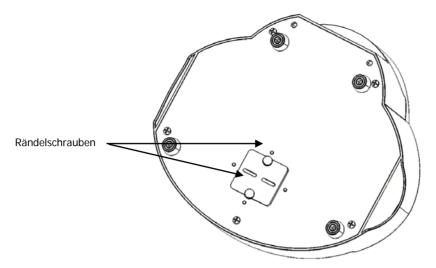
Position der Rändelschrauben zur Befestigung des Probenhalters
